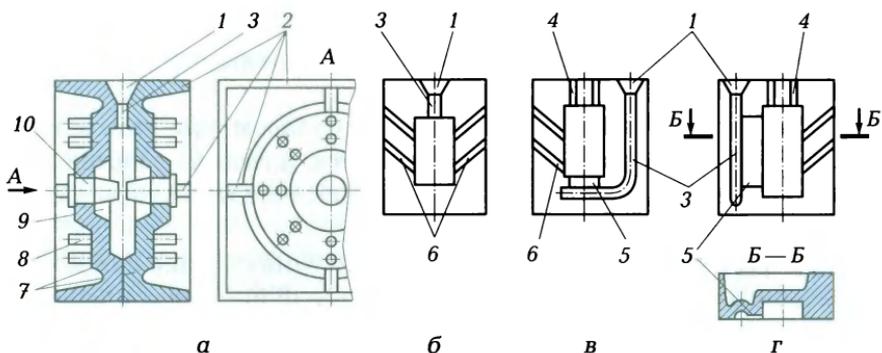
Двухстворчатый кокиль (а) и схемы заливки кокилей (б–г):
